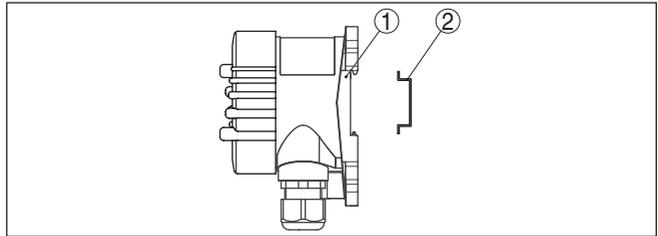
VEGABOX 03 con carcasa plástica para el montaje en regletas de montaje
